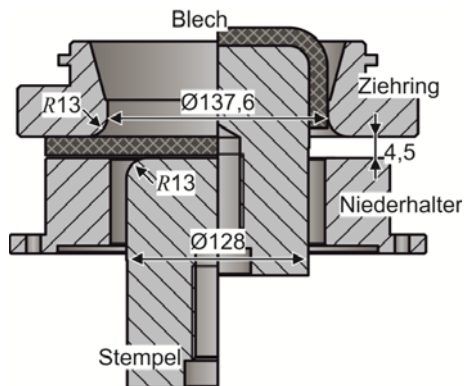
Werkzeugaufbau für das Tiefziehen der Bleche mit Kernstruktur (Abmessungen in mm)
